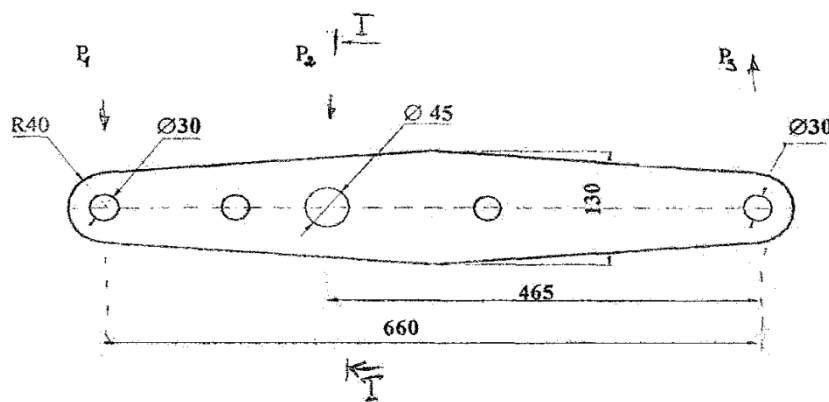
Розрахункова схема горизонтального важеля (розміри)
